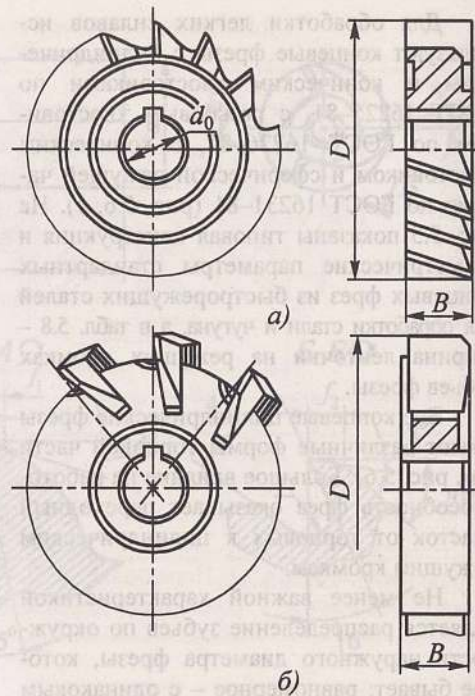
Фрезы дисковые двухсторонние: а – цельные; б – со вставными ножами
